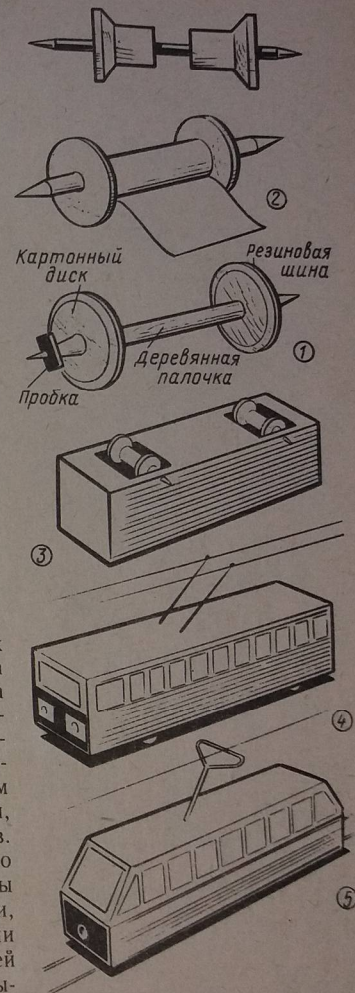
Изготовление моделей из готовых коробок: 1 — изготовление колес; 2 — увеличение длины катушки для колес; 3 — установка колес; 4 — модель троллейбуса; 5 — модель трамвая
